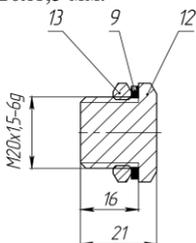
Устройство заглушки Exd КВВ-ЗГд20
